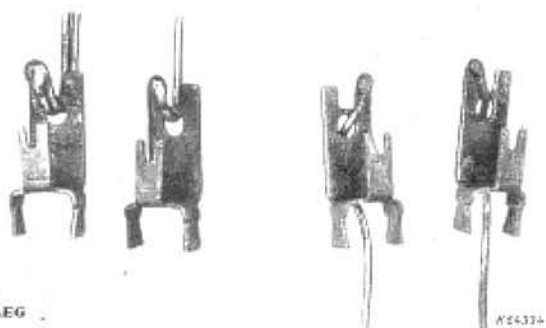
Verschweißung von Kupferdraht an verkupferte Eisenösen.
